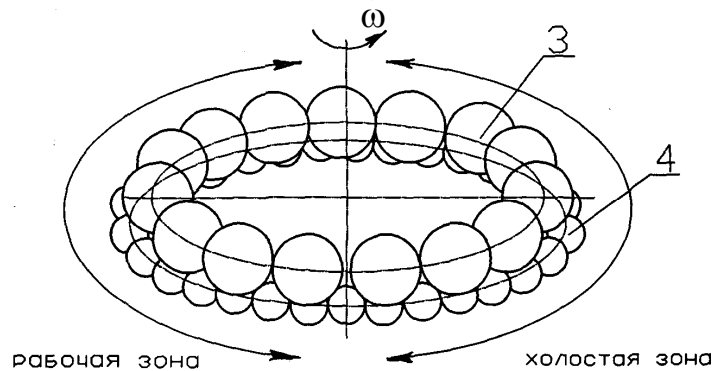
Схема движения приводящих (3) и деформирующих (4) шаров в кольцевой камере инструмента [1]
